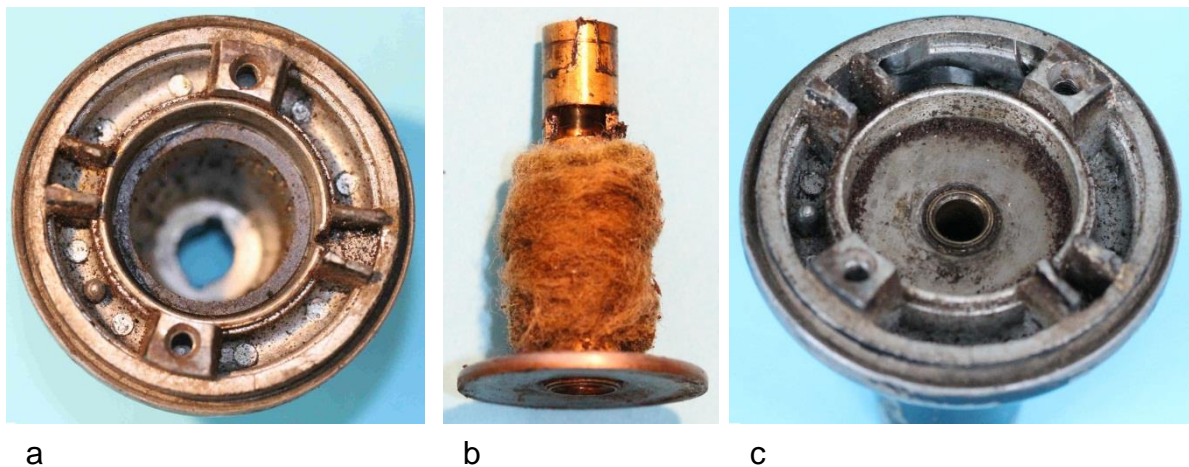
Lager: a) Alugusslagerhals, b) Lagerbaugruppe bestehend aus Lagerrohr, Lagerteller und Öldepot, c) Eingesetzte Lagerbaugruppe
